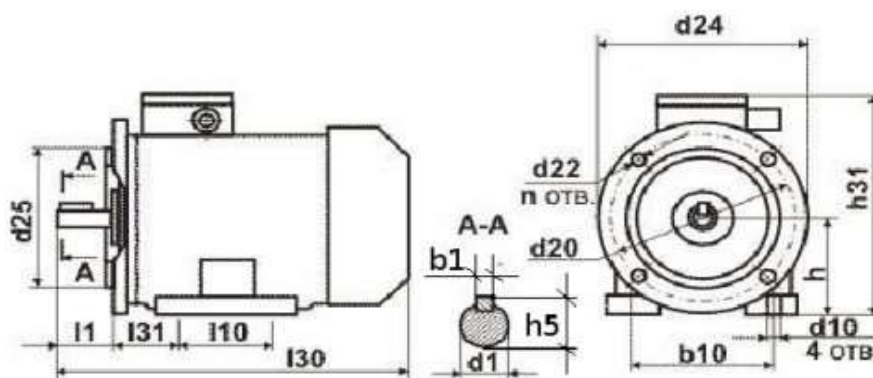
Габаритные и установочно-присоединительные размеры двигателя
